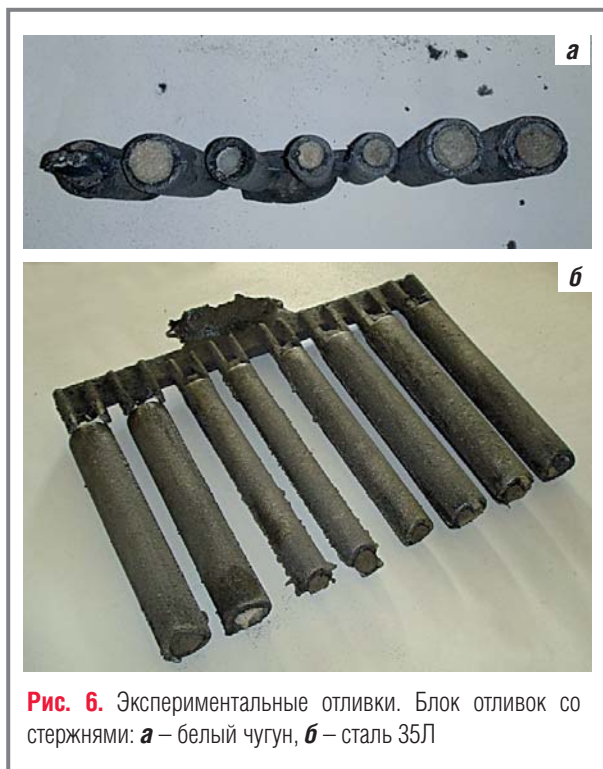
Экспериментальные отливки. Блок отливок со стержнями: а – белый чугун, б – сталь 35Л
